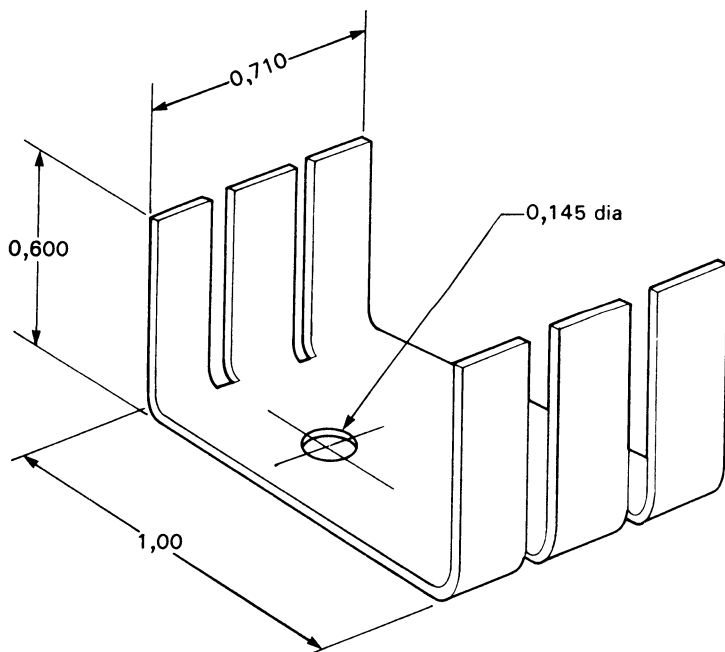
б. Радиатор для корпуса типа TO-220. (Все размеры приведены в дюймах.)
